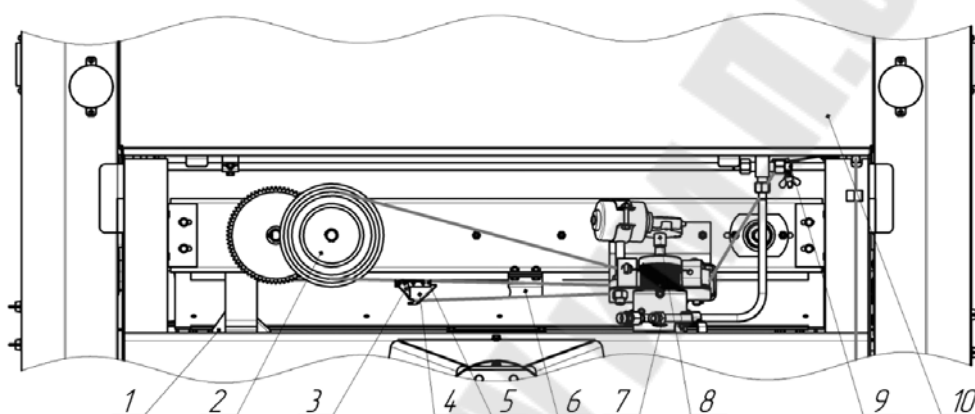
Обматывающий аппарат: 1 – поводок неподвижный; 2 – шкив; 3 – нож; 4 – поводок; 5 – каретка; 6 – упор; 7 – механизм подачи шпагата ручной; 8 – электропривод механизма подачи шпагата; 9 – тормоз шпагата; 10 – ящик для установки бобин шпагата
